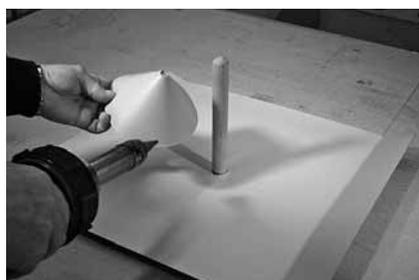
Разогревают внутреннюю и внешнюю кромки конуса.
